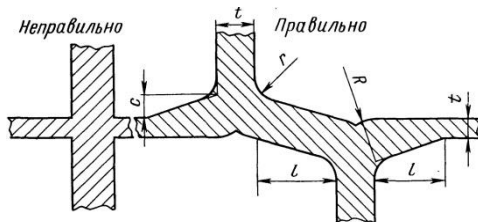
Неправильное и правильное выполнение узла пересечения стенок
